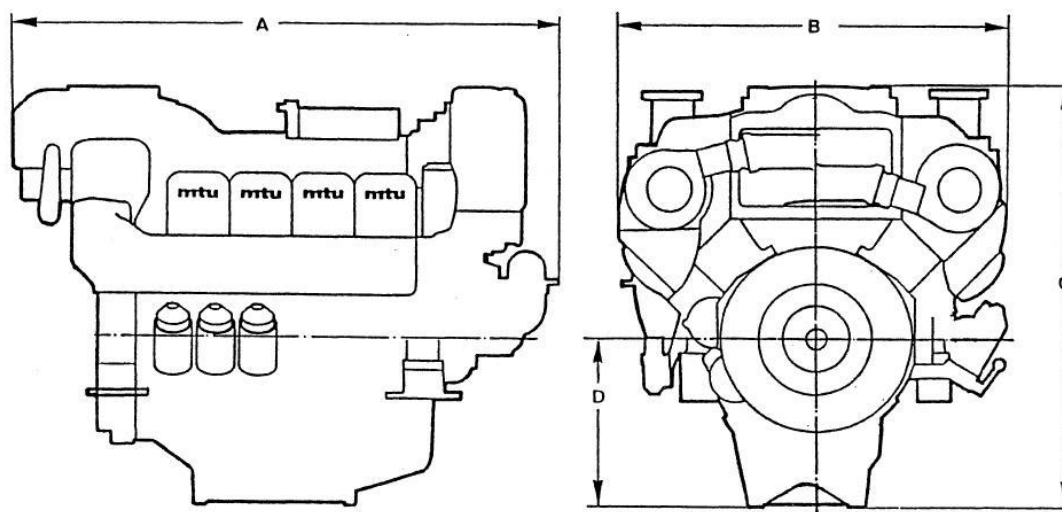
4 – Dimensões do Gerador a Diesel; Fonte: Manual MTU Diesel Engine
